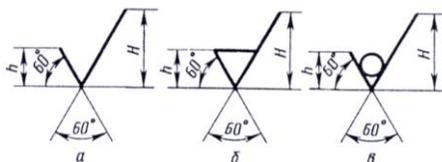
Виды знаков обозначения шероховатости поверхности
